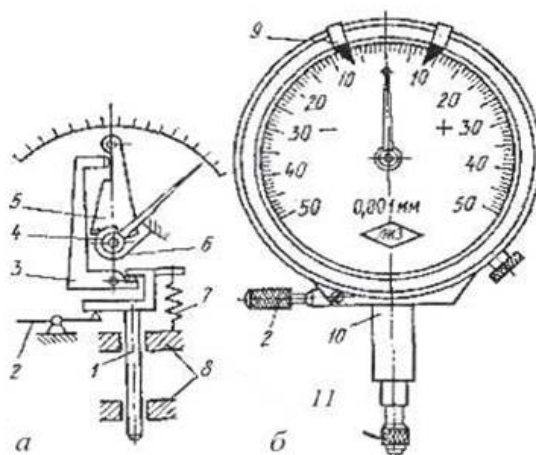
Важільно-зубчаста вимірювальна головка ІІГ (мікромір): а - схема; б - загальний вигляд: 1 - вимірювальний стержень; 2 - відвідний важіль; 3 - двоплечий важіль; 4 - зубчасте колесо; 5 - важіль з зубчастим сектором; 6 - спіральна пружина; 7 - пружина; 8 - напрямні втулки; 9 - переставні показники поля допуску; 10 - напрямна втулка (гільза); 11 - вимірювальний наконечник
